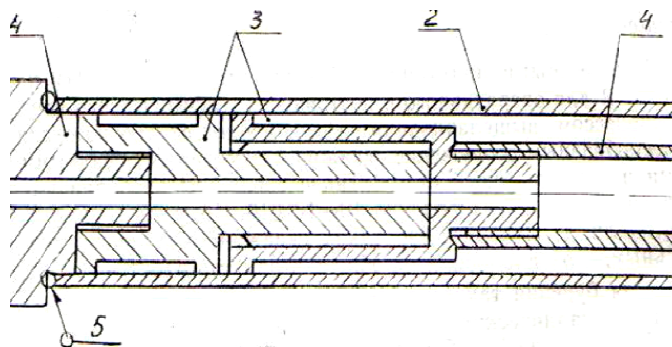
Схема бурового снаряда для установки обсадных труб в процессе бурения скважины в разрушенном массиве: 1 – буровой став; 2 – обсадная труба; 3 – шлицевой разъединитель; 4 – переходник; 5 – сварочный шов
